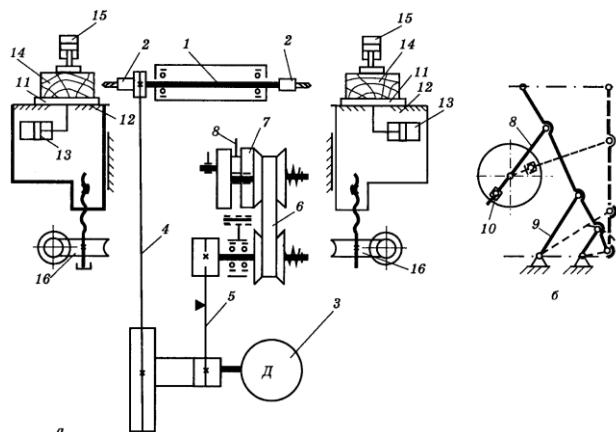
Кінематична схема двобічного свердлильно-пазувального верстата: *а* – кінематична схема; *б* – лямбдоподібний механізм коливання шпинделя: 1 – шпиндель; 2 – патрони; 3 – електродвигун; 4 – плоскопасова передача; 5 – клинопасова передача; 6 – клинопасовий варіатор; 7 – барабан; 8 – шатун; 9 – шарнірно-важільна система; 10 – повзун; 11 – стіл; 12 – напрямні; 13 – пневмоциліндр; 14 – заготовки; 15 – пневмопритискачі; 16 – черв'ячно-гвинтовий механізм
